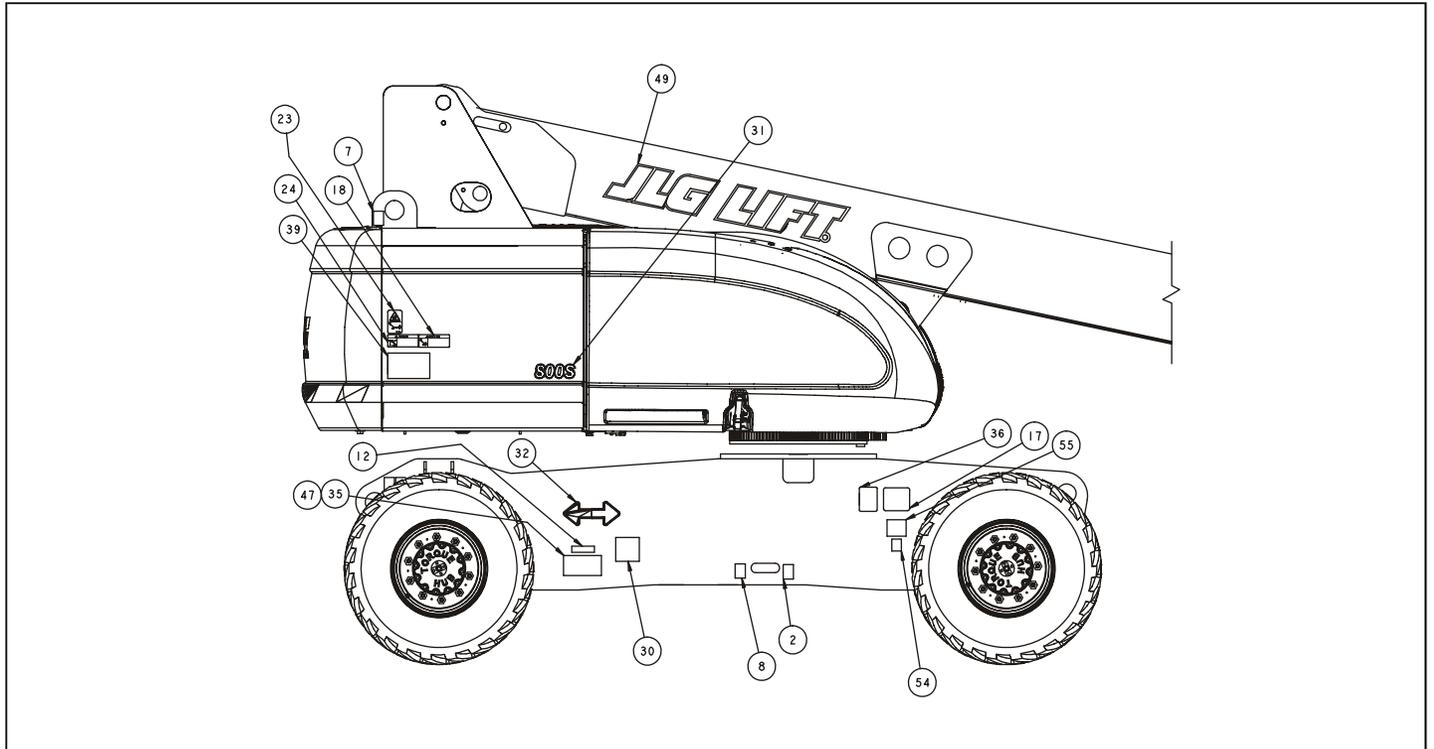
标贴位置 - 侧入式平台 - 图 1/5
